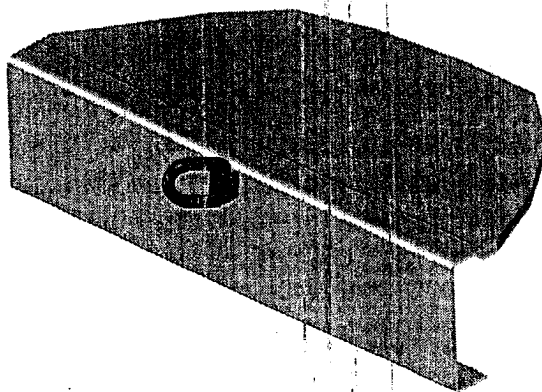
Argolla D soldada (eje perpendicular al suelo)
